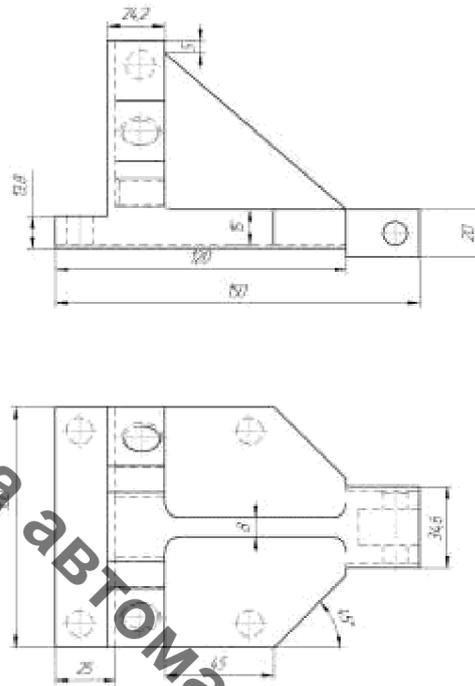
Ескіз заготовки в оболонковій формі
